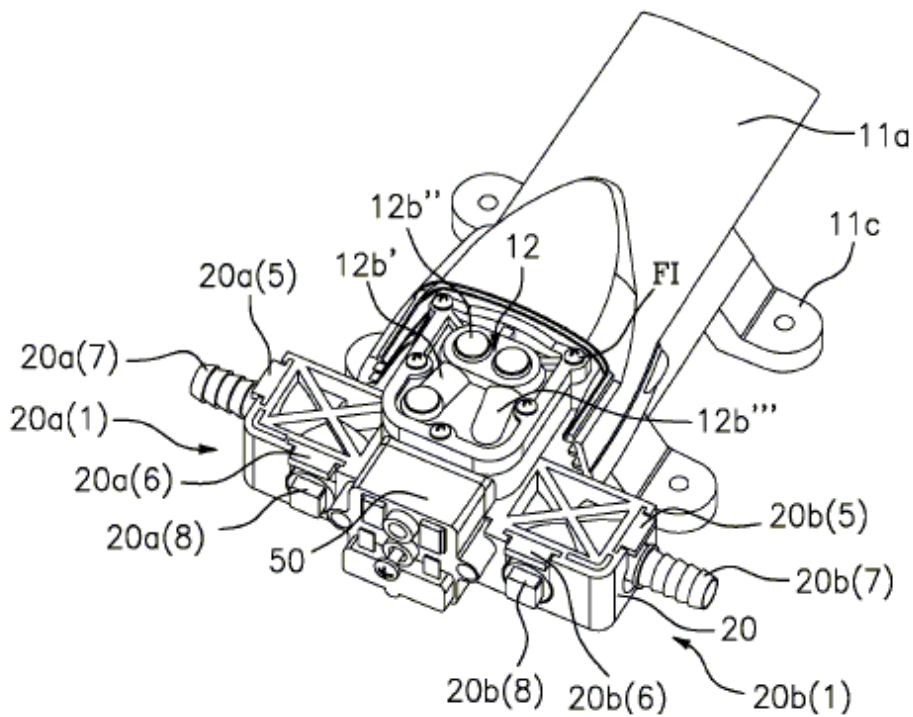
A: Conjunto de bomba que presenta una conexión de accesorio de puerto izquierda / derecha estándar
